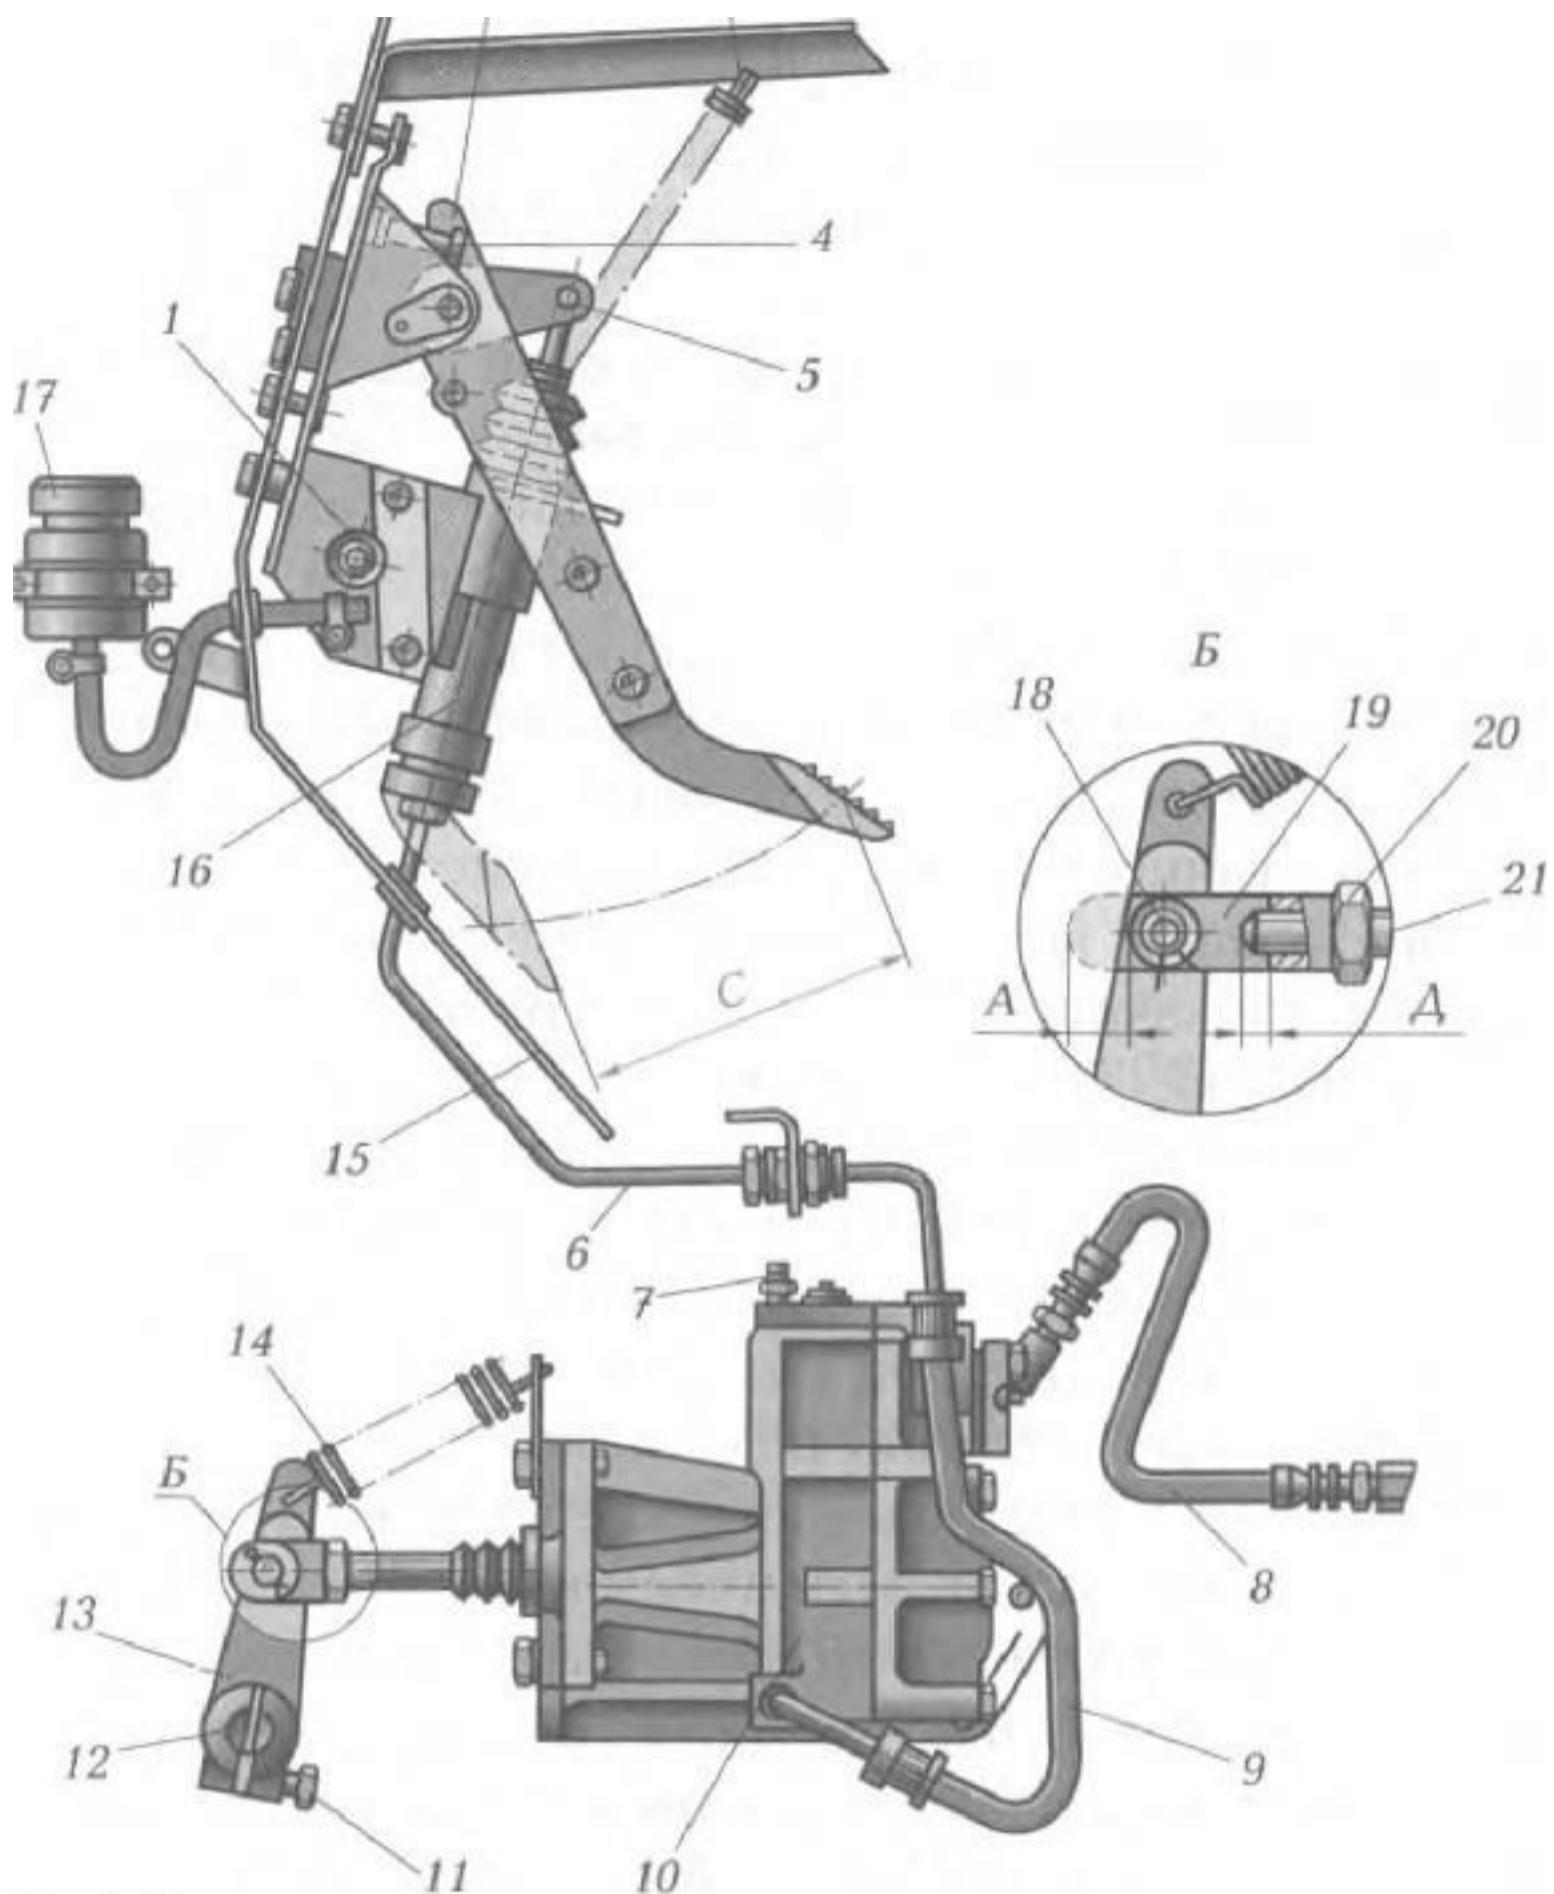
Регулировка сцепления с пневмогидравлическим приводом:
